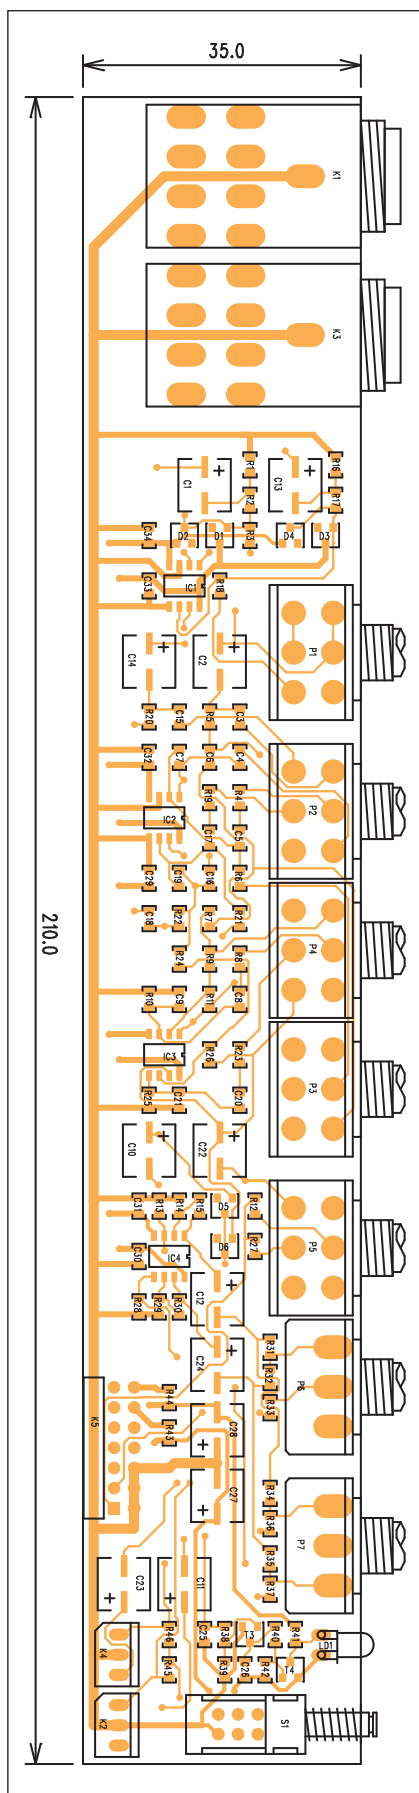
Obrazec desky spojů mikrofonního vstupu (strana BOTTOM)
